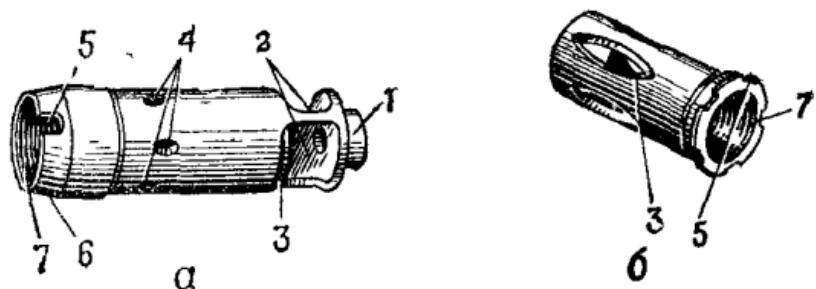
Дульный тормоз-компенсатор и пламегаситель:
